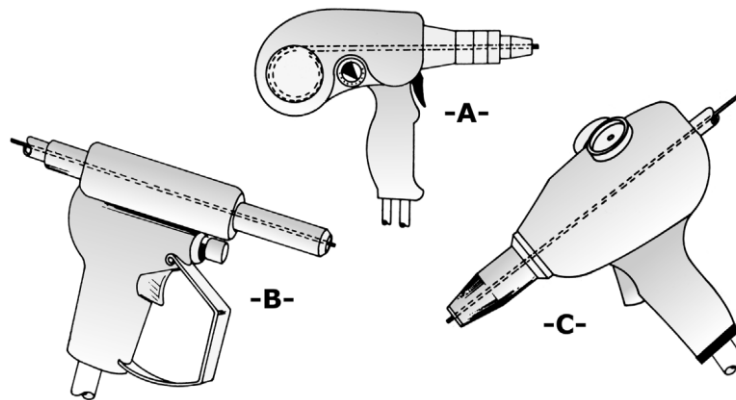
Ilustraciones de los tipos de pistolas para soldadura MIG.
